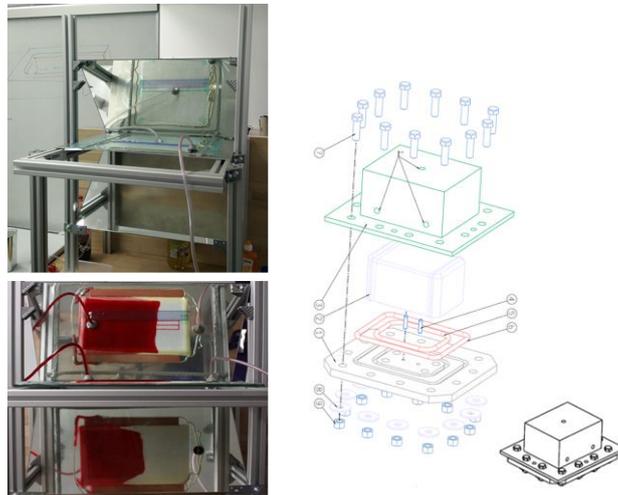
Infusionsteststand (links oben) mit Experiment zur Demonstration des Lead-lags bei Vakuuminfusion (links unten) und Explosionszeichnung vom RTM-Werkzeug (rechts).
